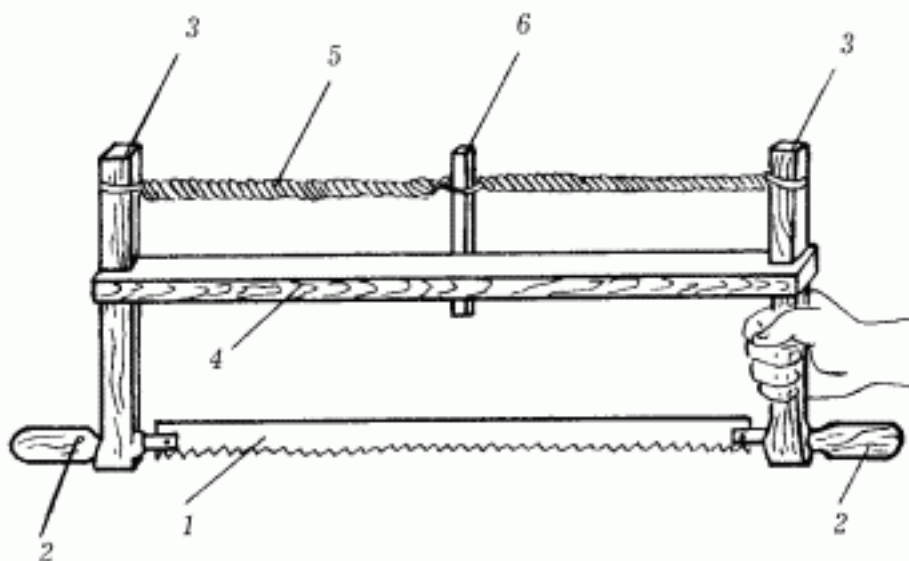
Лучковая пила: 1 – пильное полотно; 2 – ручки; 3 – стойки; 4 – распорка; 5 – тетива; 6 – закрутка.
